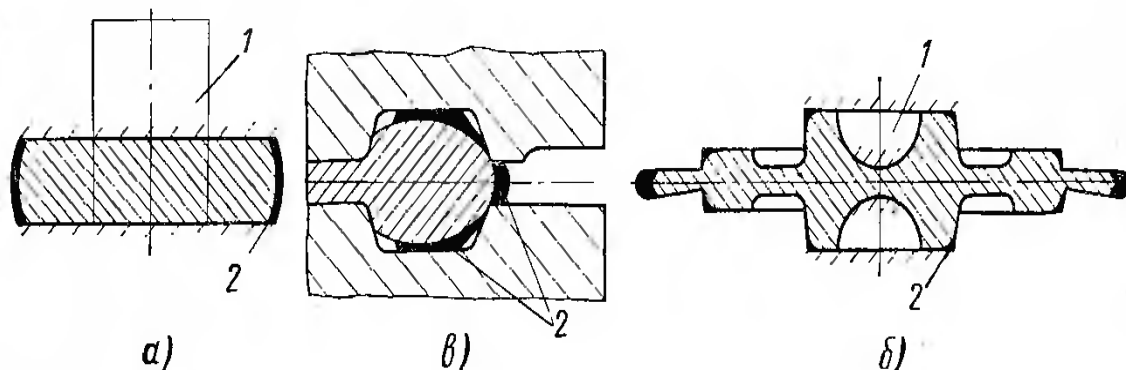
Схема распределения стекла в поковках: *а* – на заготовке после осадки; *б* – в поковке шестерни; *в* – на ободке в процессе штамповки; 1 – пленка стекла; 2 – скопление стекла
